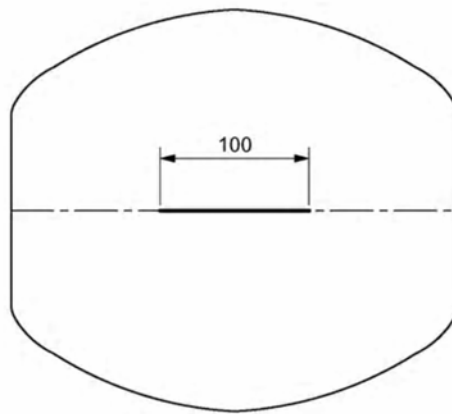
Extensión de radiografía de las soldaduras. Botellas únicamente soldadas circunferencialmente
